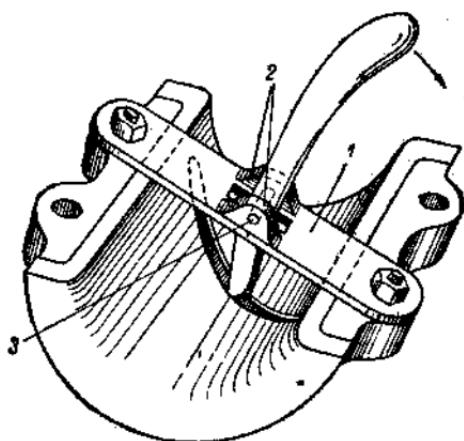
Приспособление для прострагивания канавок в подшипниках.
